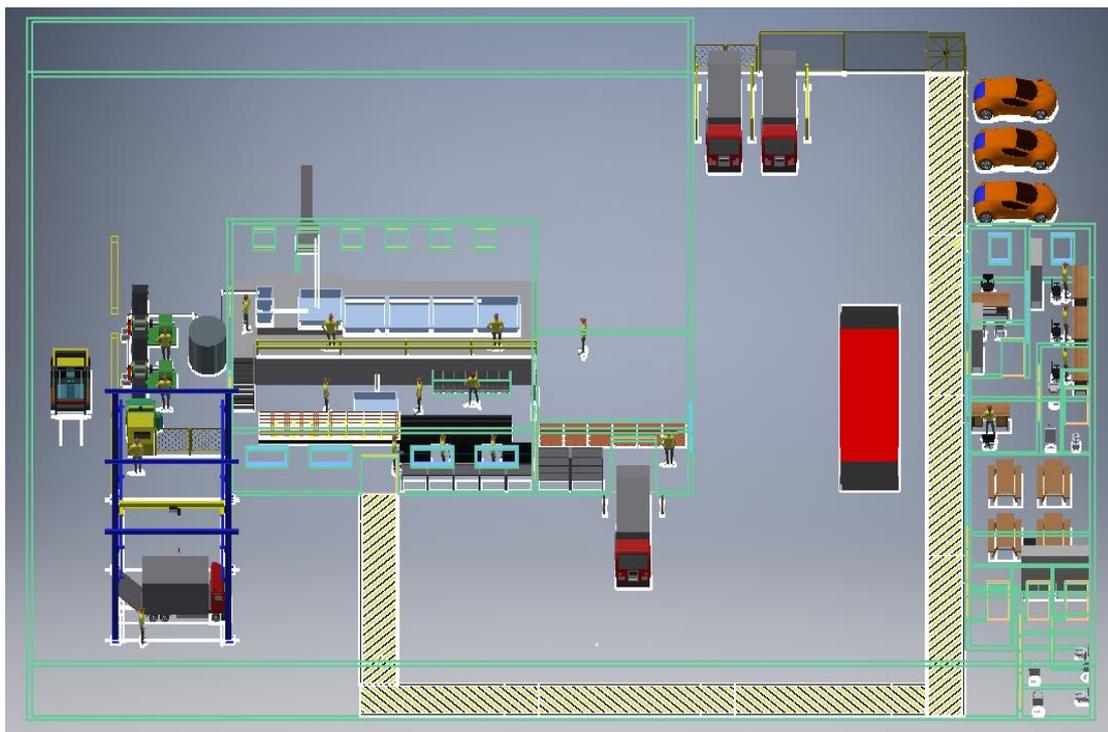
Vista superior trasera del rediseño de planta propuesto.
